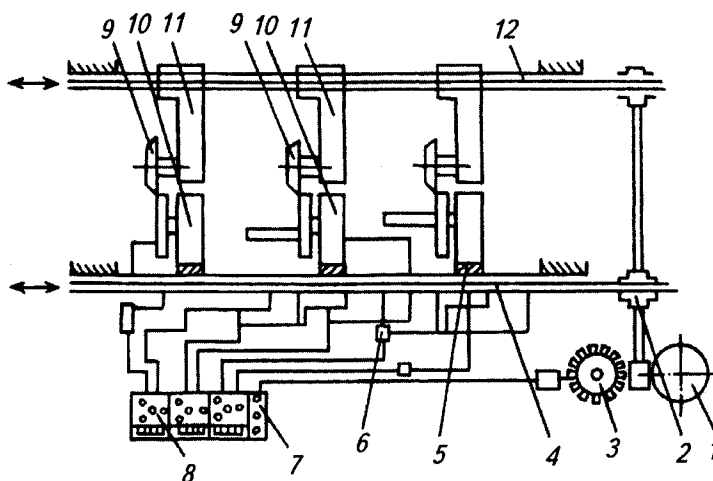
Схема сдвоенного продольно-резательного станка:
